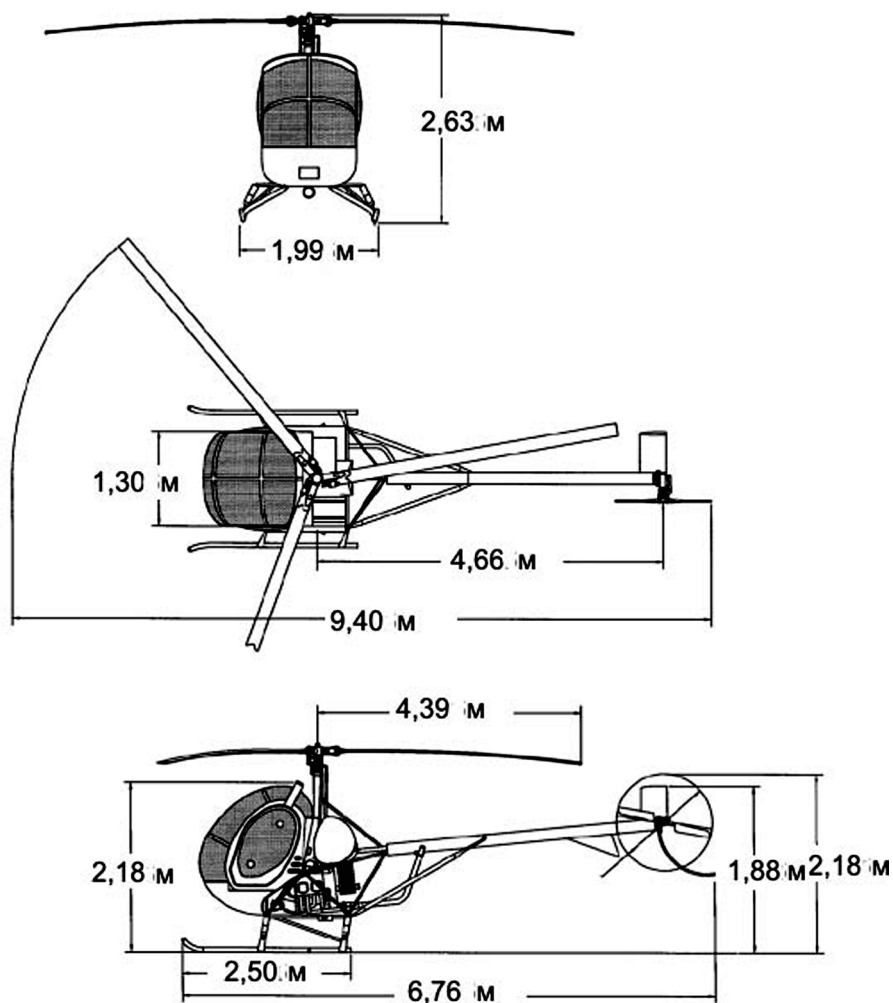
Схема вертолета Schweizer 300CB
